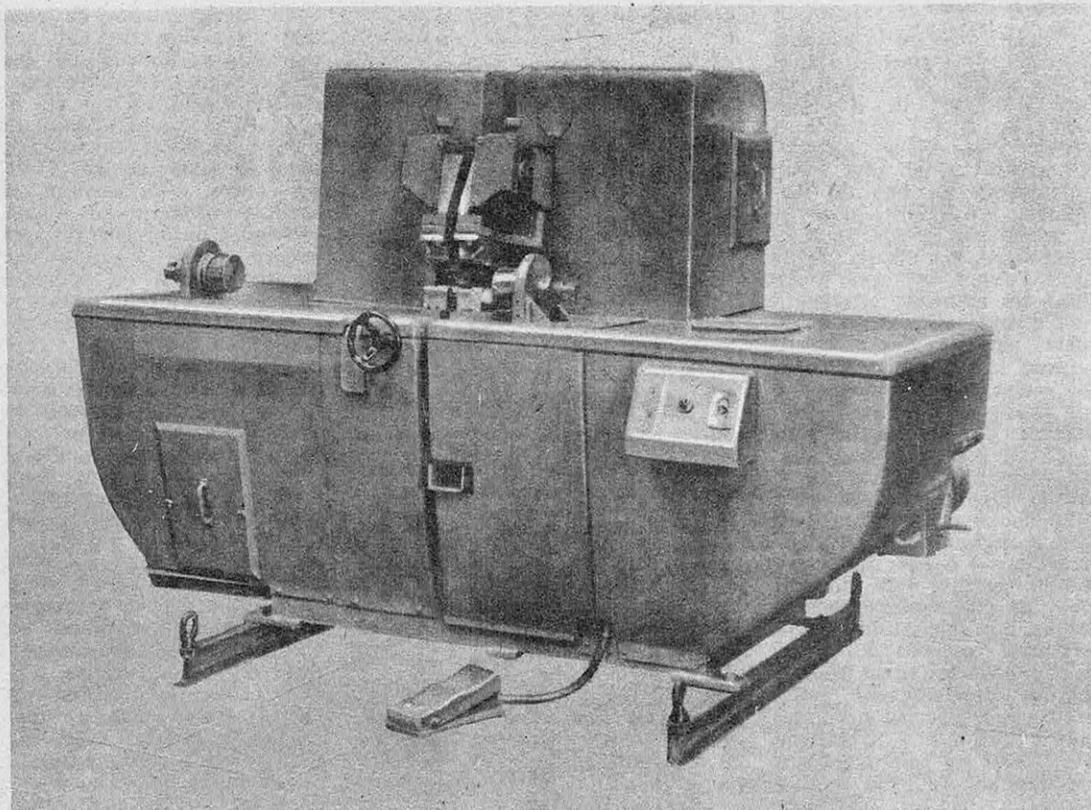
MACHINE A SOUDER EN BOUT AUTOMATIQUE (LA SOUDURE ÉLECTRIQUE)
